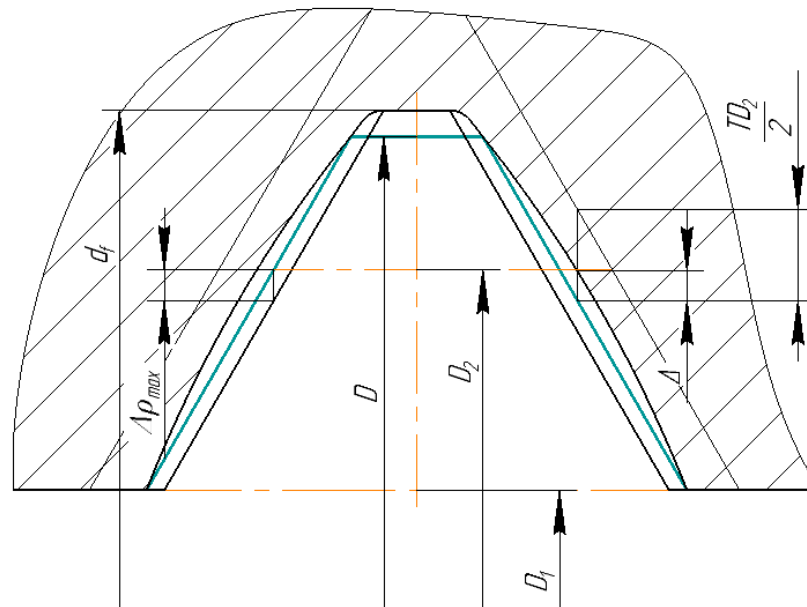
Сравнение номинального профиля резьбы и профиля, полученного при моделировании процесса резьбофрезерования:  $\Delta\rho_{\max}$  – величина геометрической погрешности профиля;  $\Delta$  – величина прогиба боковых сторон;  $D$  – номинальный диаметр внутренней резьбы;  $D_1$  – внутренний диаметр резьбы;  $D_2$  – средний диаметр резьбы;  $TD_2$  – поле допуска на средний диаметр резьбы.
